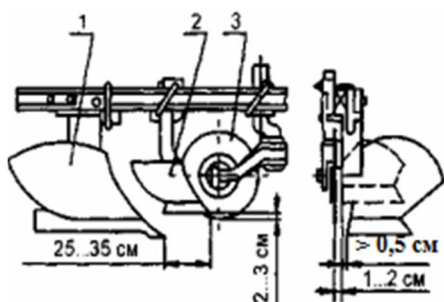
Относительное размещение предплужника и дискового ножа на раме плуга: 1 - корпус; 2 - предплужник; 3 - дисковый нож.
